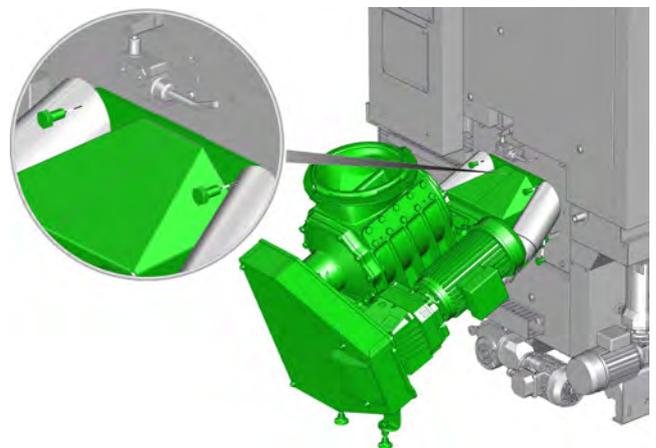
Joint d'étanchéité sur la bride de la vis d'alimentation
